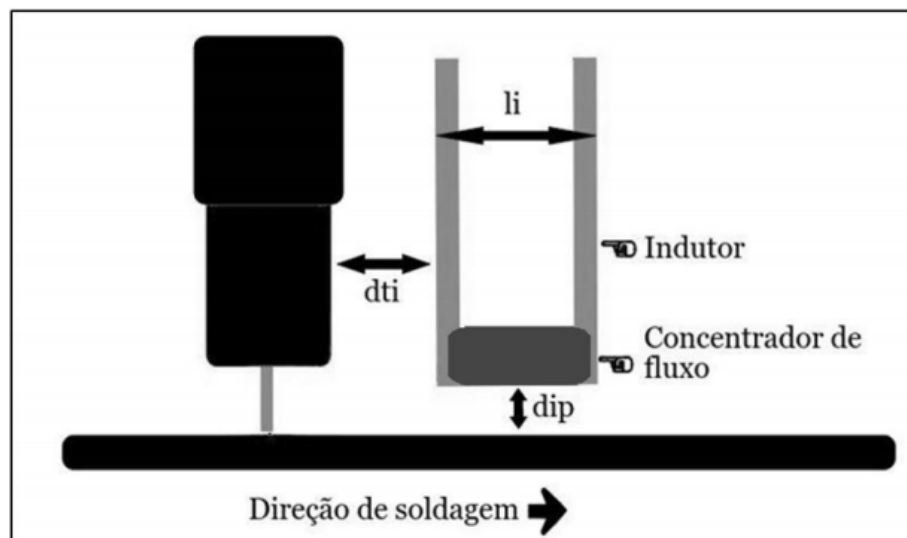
Esquema da montagem em tandem de um sistema de soldagem MIG/MAG com pré-aquecimento
